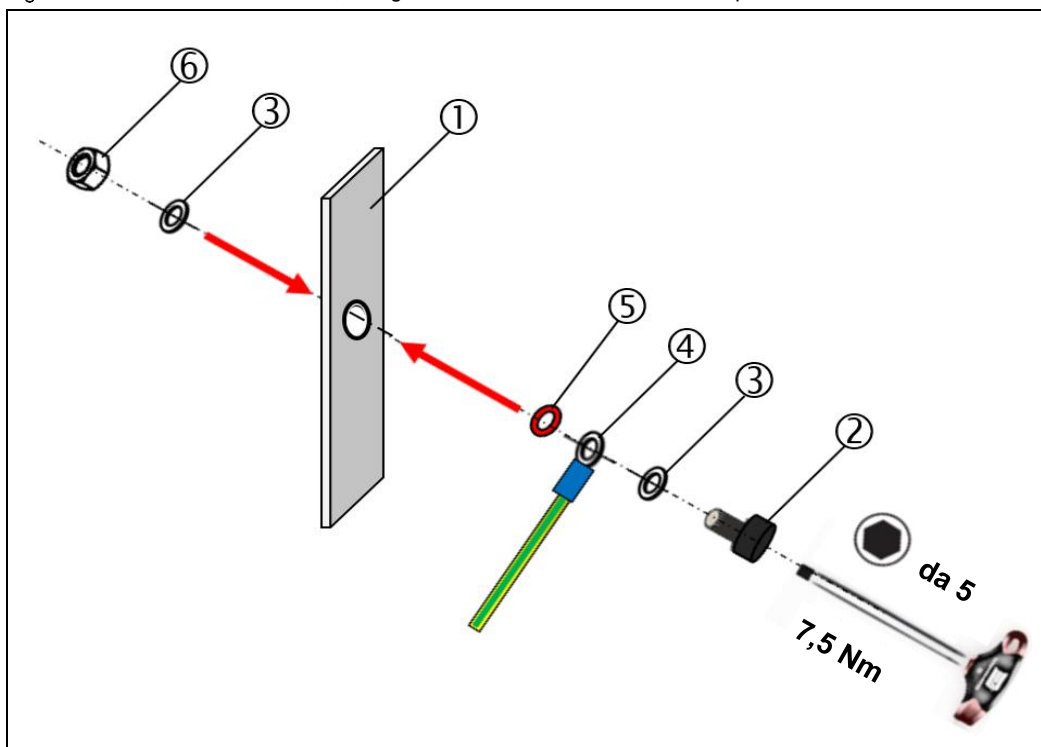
Montaggio collegamento di messa a terra, VN2020
